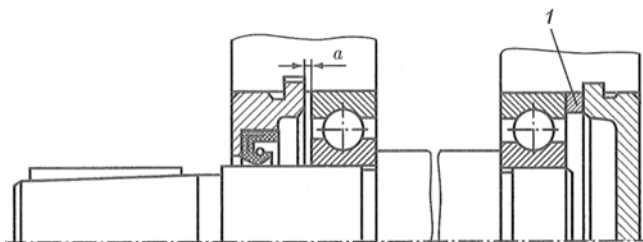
Пример конструкции подшипникового узла с закладными крышками подшипников
